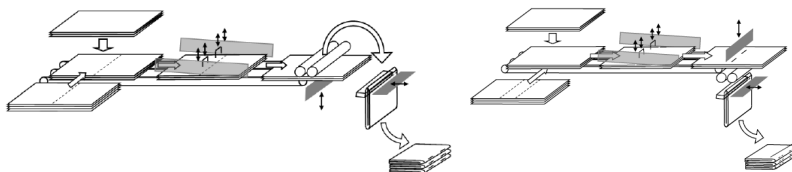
Схемы оборудования для изготовления брошюр и блоков
